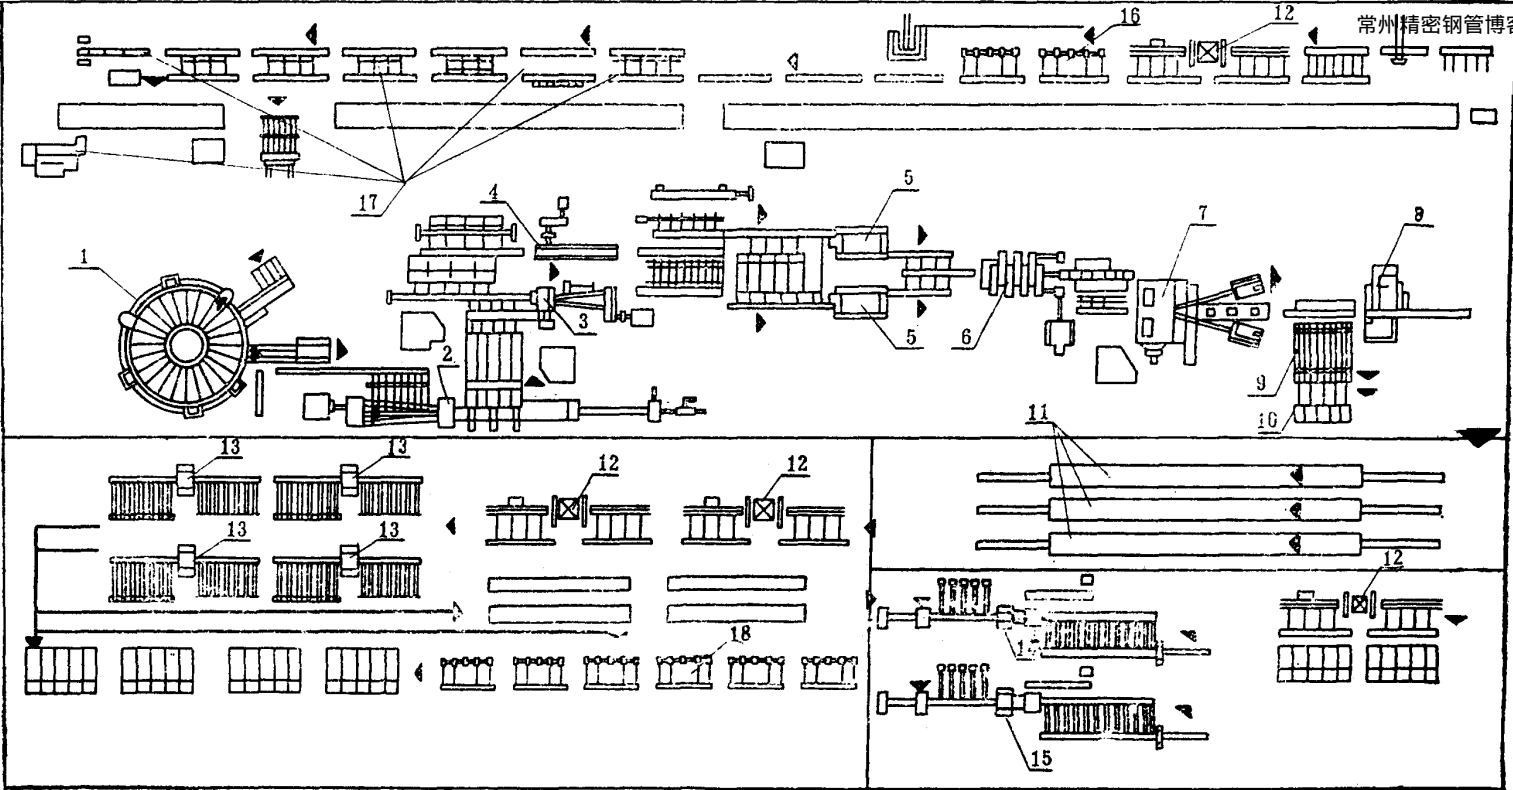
西德克雷弗尔德厂一号三辊轧管机组平面布置图
